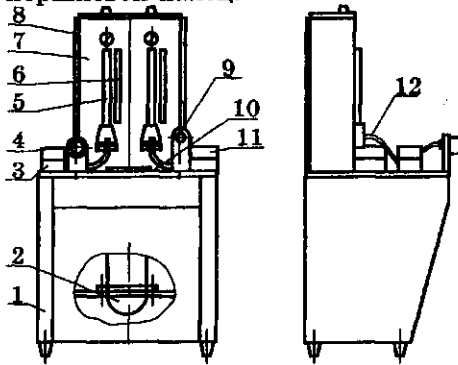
Схема станда для сортировки шатунов на размерные группы: 1 — корпус; 2 — баллон;
